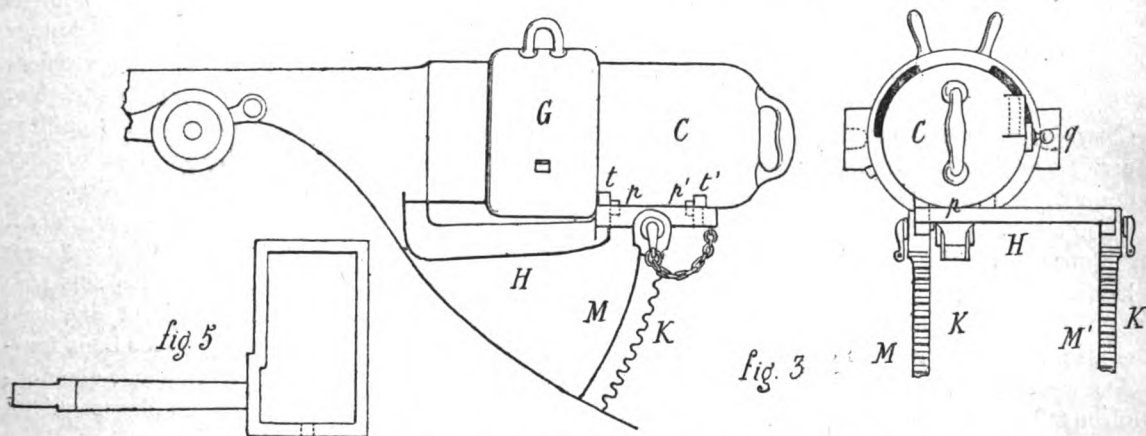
La culasse fermée, la pièce chargée. — Fig. 5. — Le châssis
